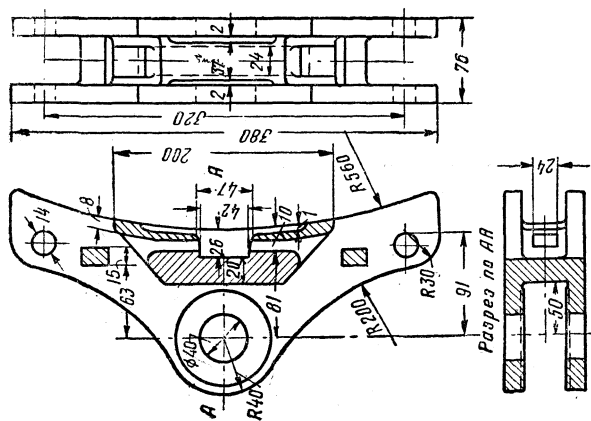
Башмак с посадкой на круглую цапфу и чековым креплением колодки
